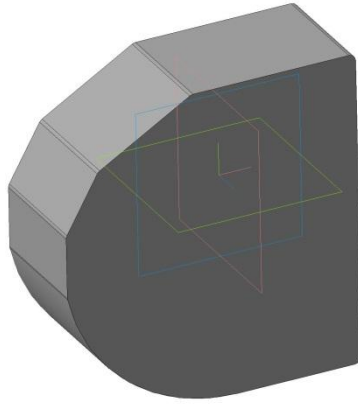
Математическая модель заготовки, построенная для вычисления массы заготовки
